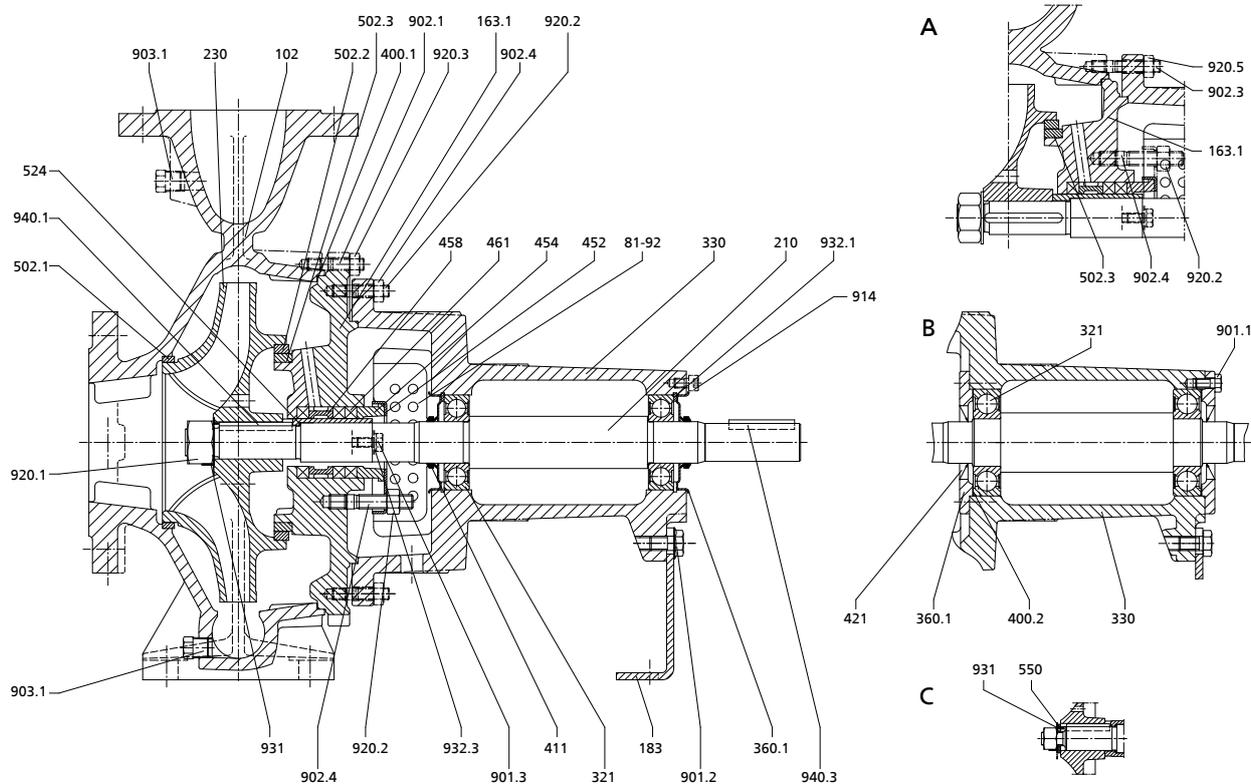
Обзорный чертеж Etanorm-MX с сальниковой набивкой
